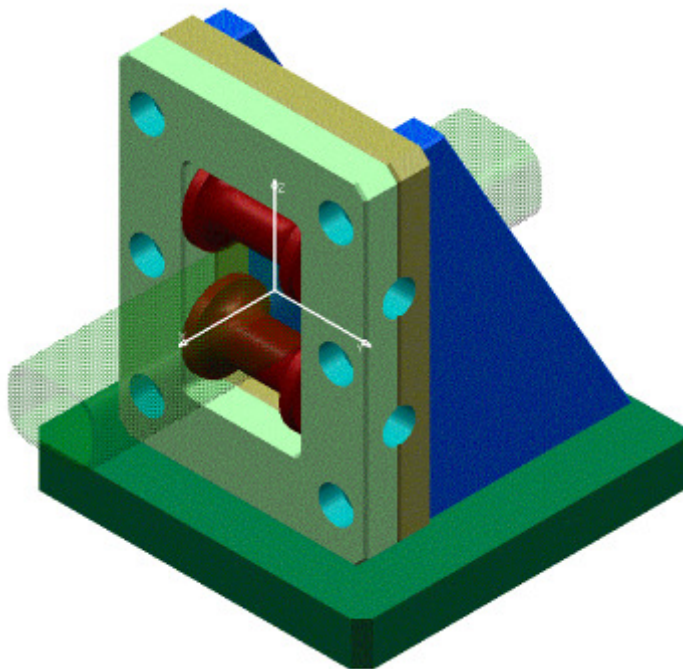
3D CAD-Konstruktion der Biegematrize (Demonstratorwerkzeug)
